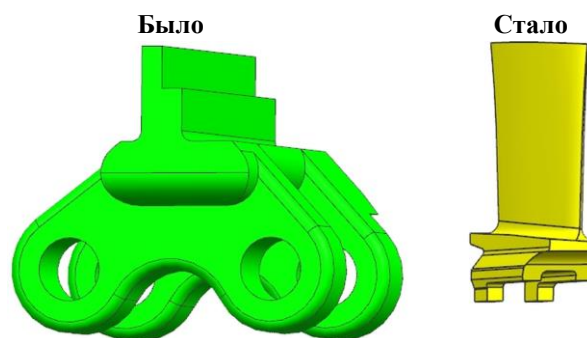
Имитатор рабочей лопатки и лопатка КВД 7 ступени Д-18Т
